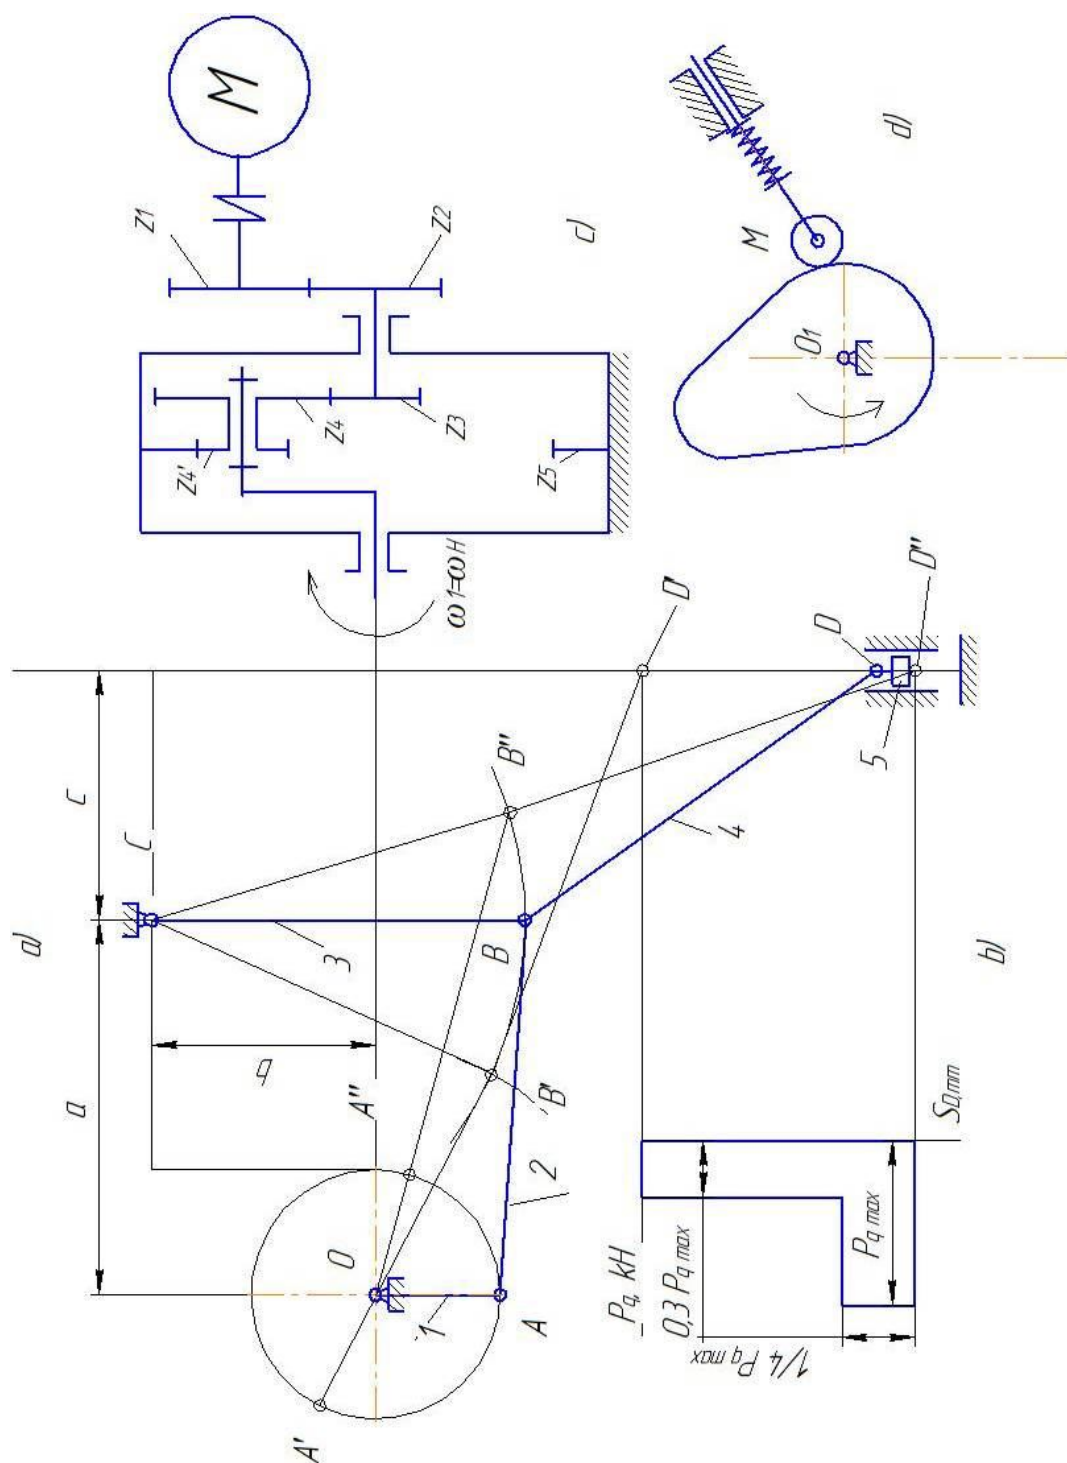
Кинематическая схема кованочно-штамповочного пресса
